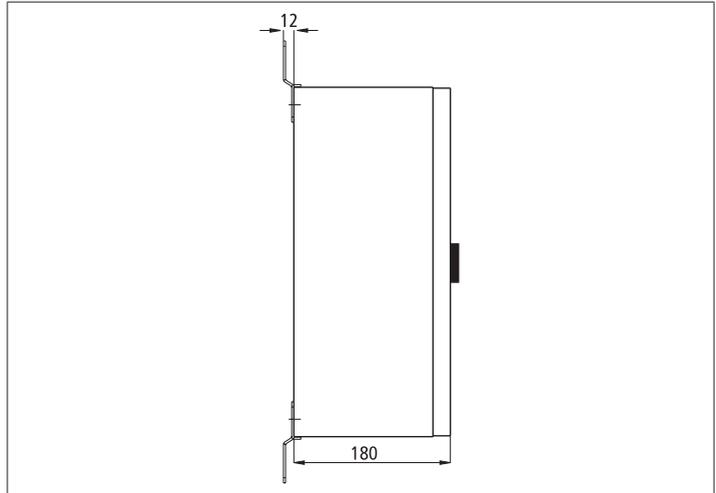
Seitenansicht SVG 522 mit Befestigungslaschen
